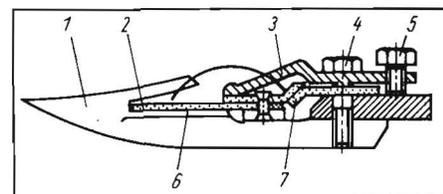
Schnitt durch einen modernen Fingermähbalken:
